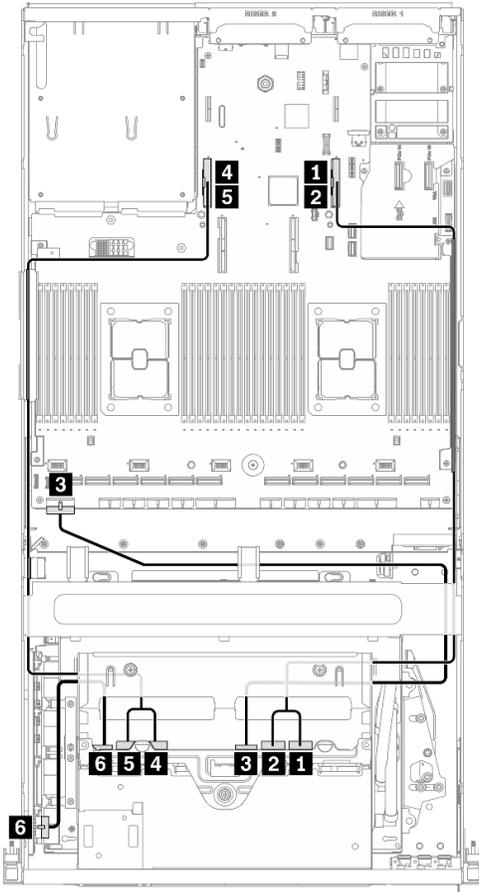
Instradamento dei cavi del backplane dell'unità - Configurazione F
